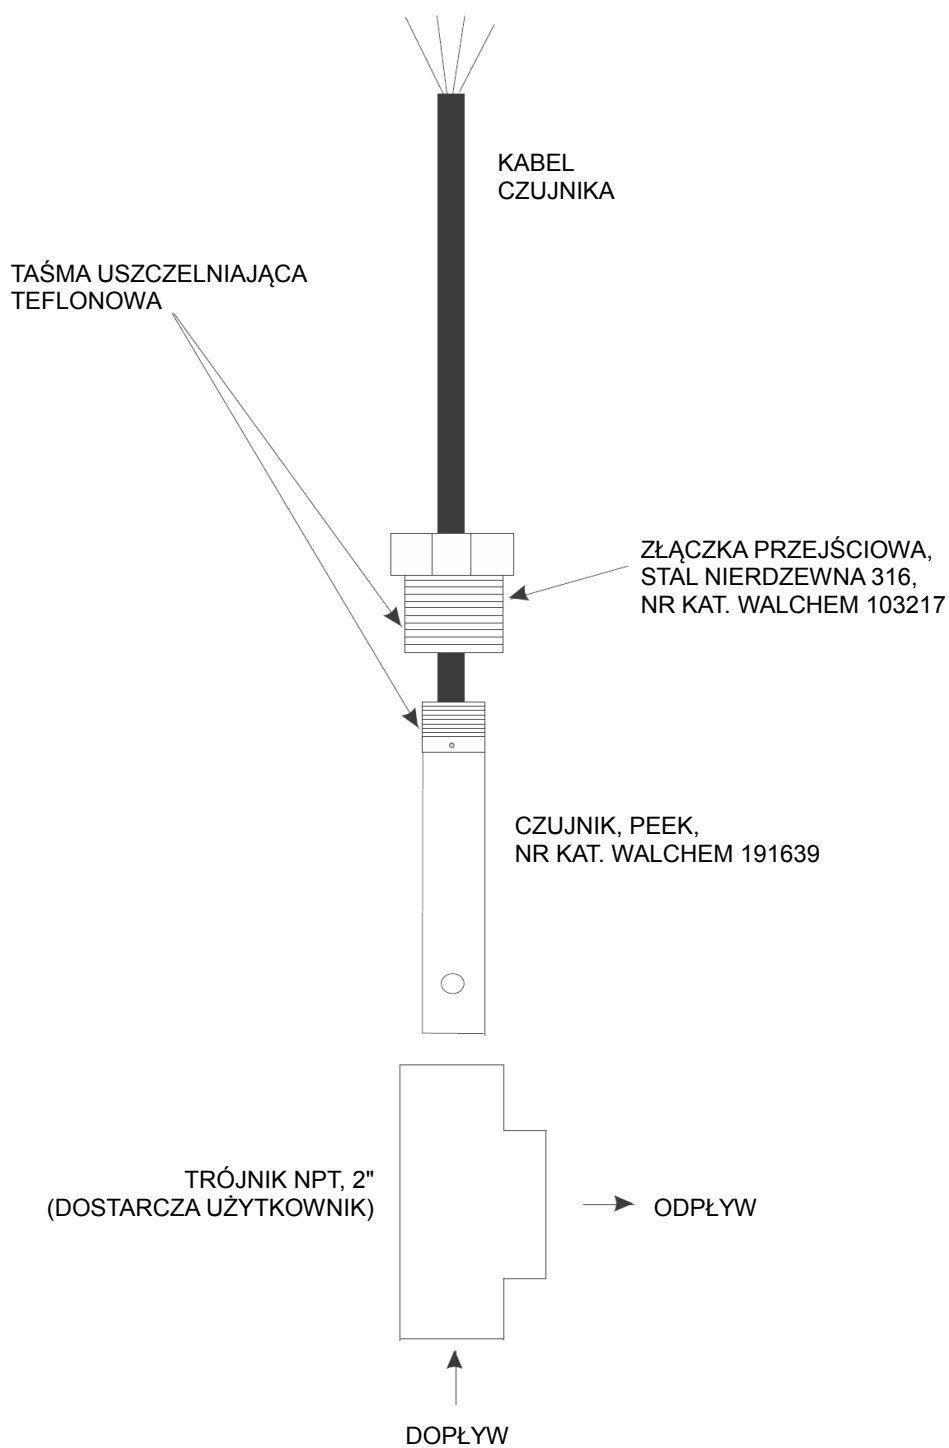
Instalacja zanurzeniowa, nr kat. 191638 i 191639
